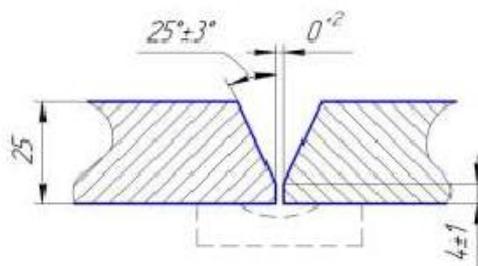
Конструктивные элементы подготовленных кромок сварного соединения
